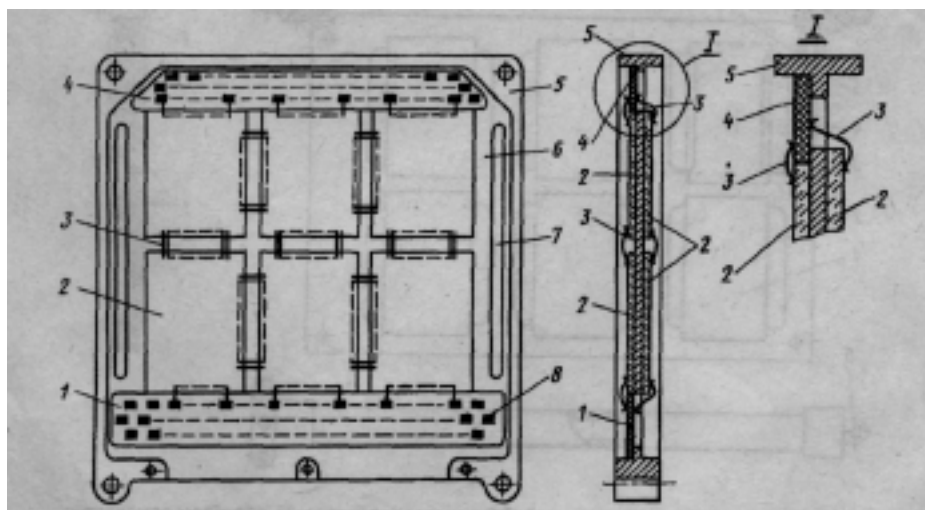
Конструкция двухсторонней ФЯ на металлической рамке: 1 — нижняя печатная вставка; 2 — микросборка; 3 — соединительный проводник; 4 — верхняя печатная вставка; 5 — рамка; 6 — планка; 7 — выступ; 8 — контактная площадка
